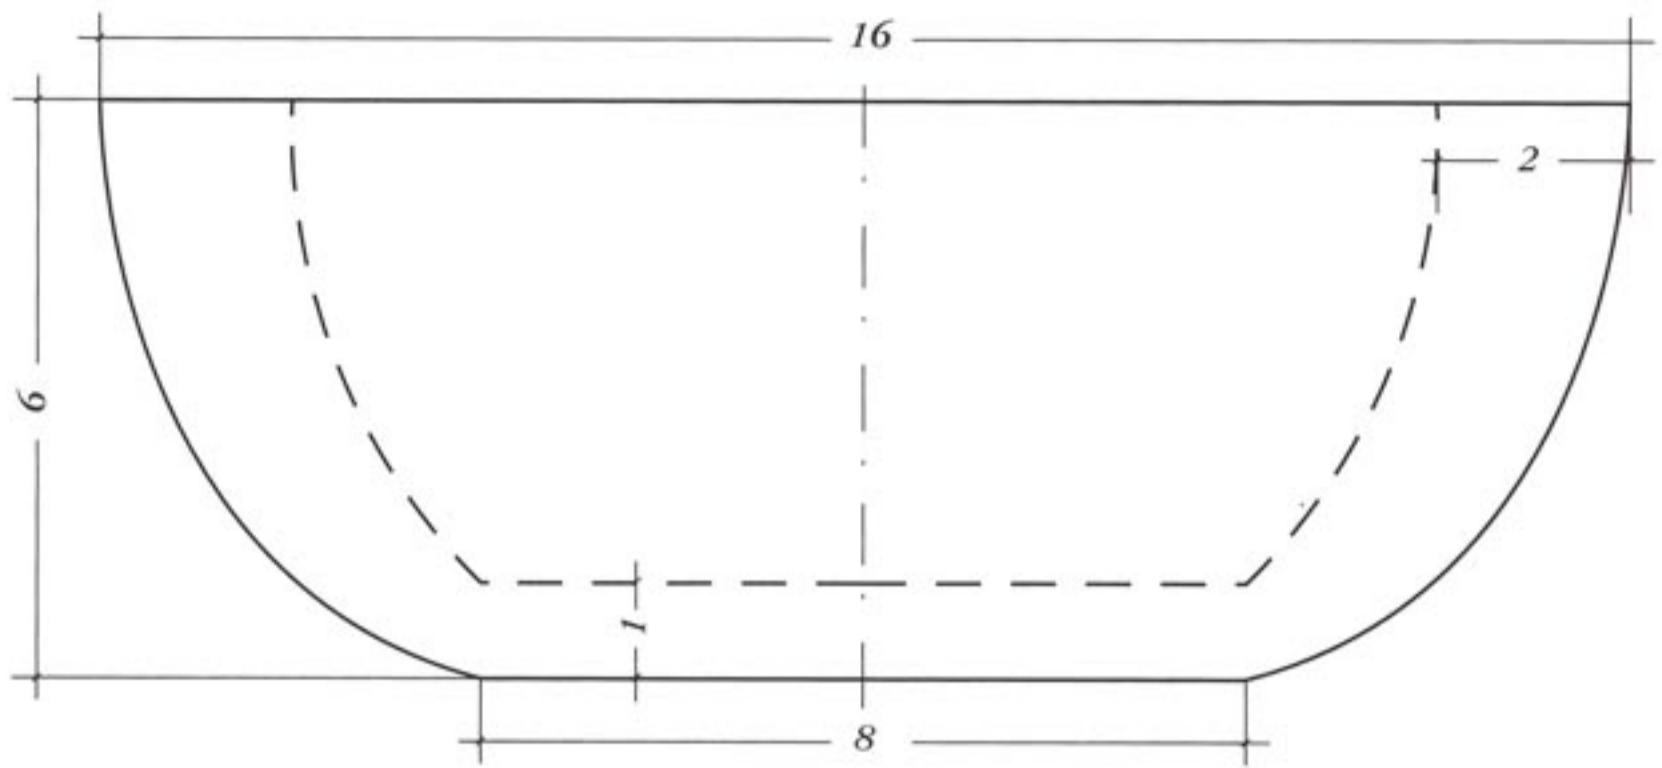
Чертеж и схемы разметки верхней части цветка чаши-вазы к рис. 192
